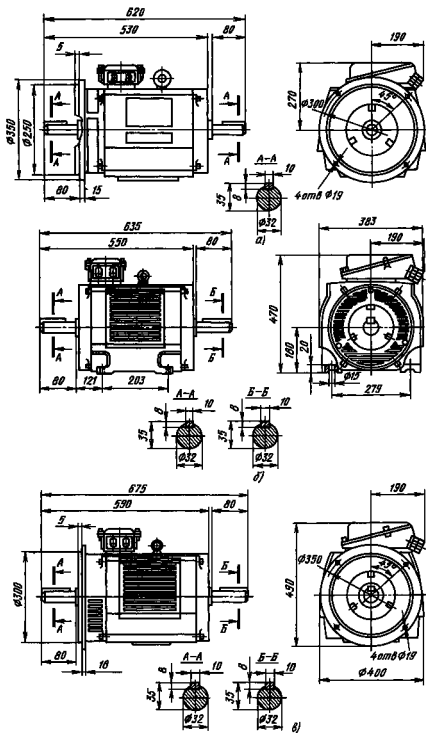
13 Габаритные, установочные и присоединительные размеры лифтовых двигателей серии 4А
